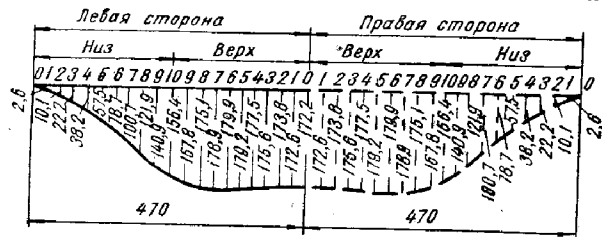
Развертка конца отрезка сварного тройника.
